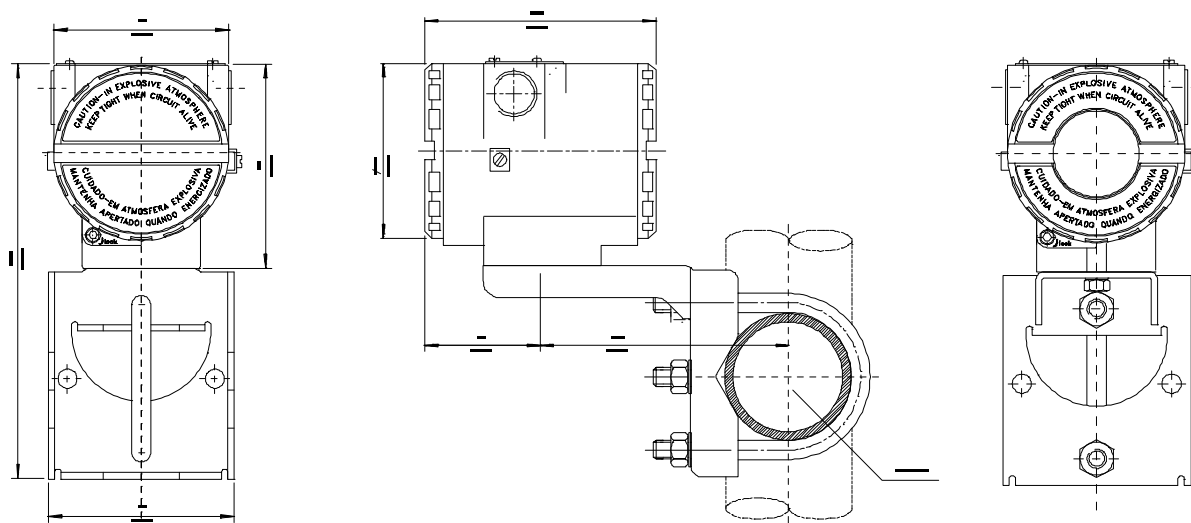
Posições de Montagem e Desenho Dimensional
